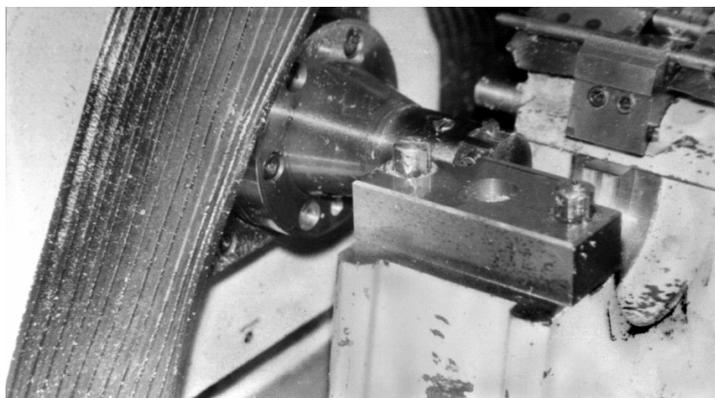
Приспособление для растачивания вкладышей коленчатого вала на станке мод. КК-4401
